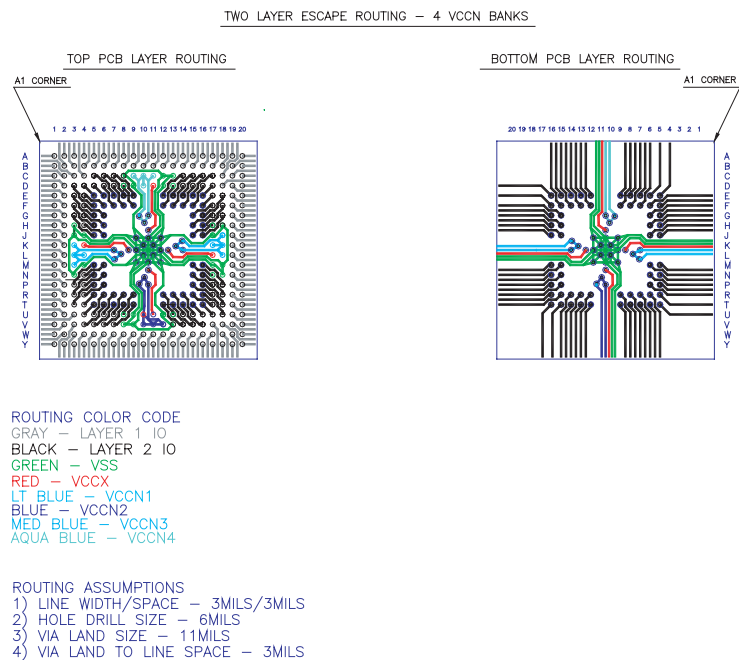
0.5mm 256 引脚 MBGA 的两层 PCB 布板方案实例
